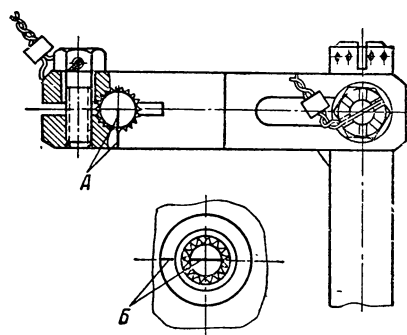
Установка рычага рычажного механизма управления регулятором:
